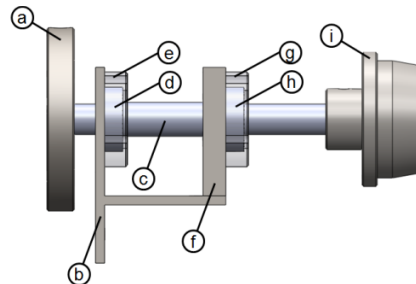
Mecanismo A - sistema de sujeción y desbobinado.
